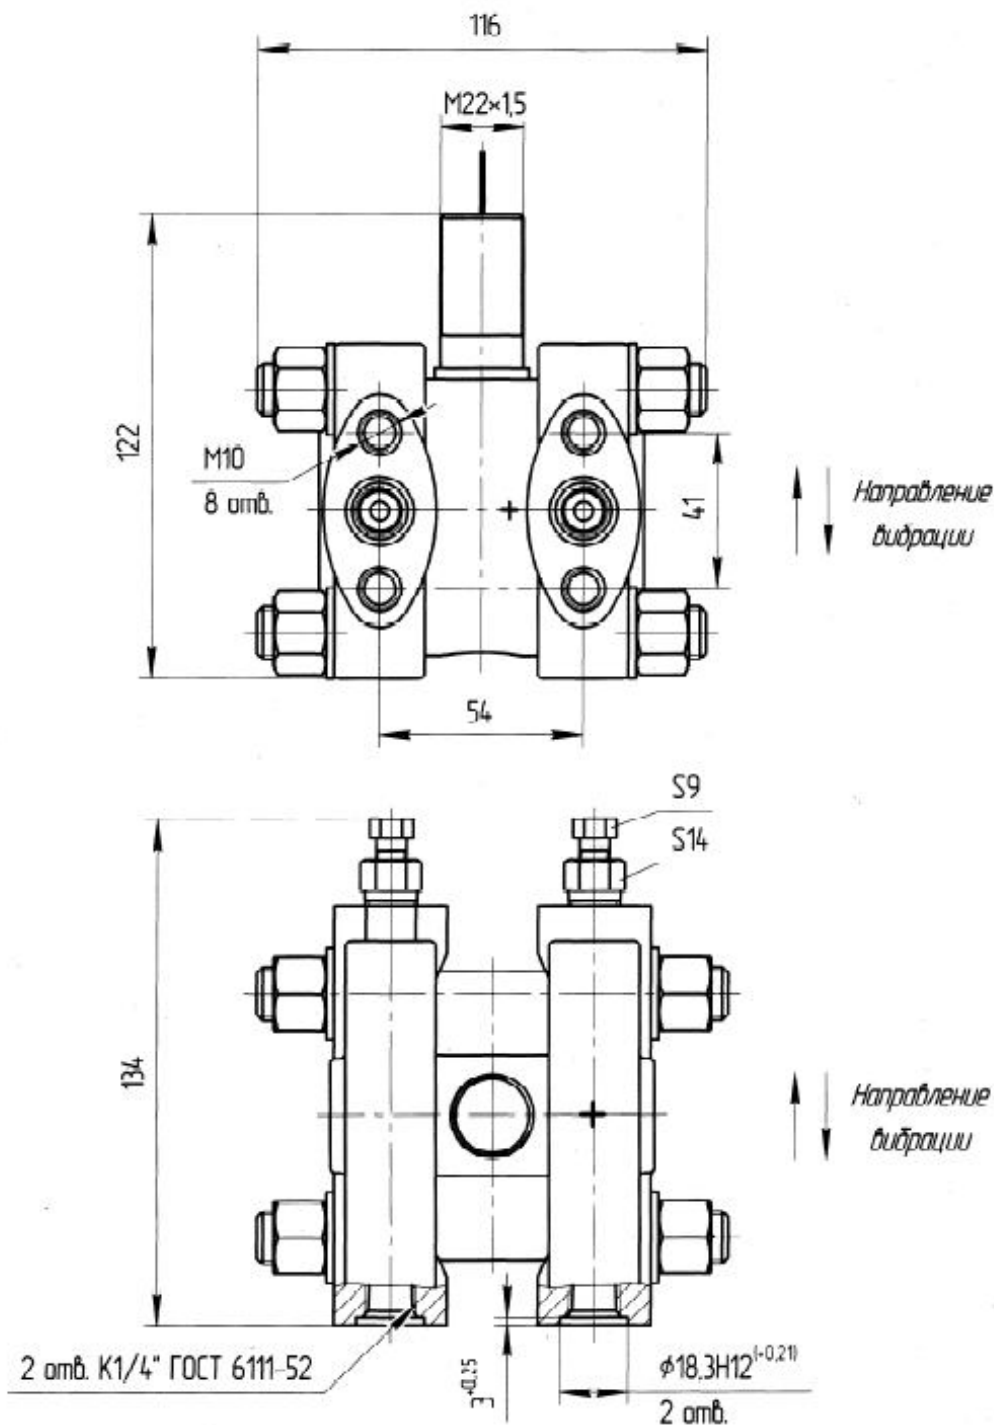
Габаритные и присоединительные размеры преобразователя разности давлений.
